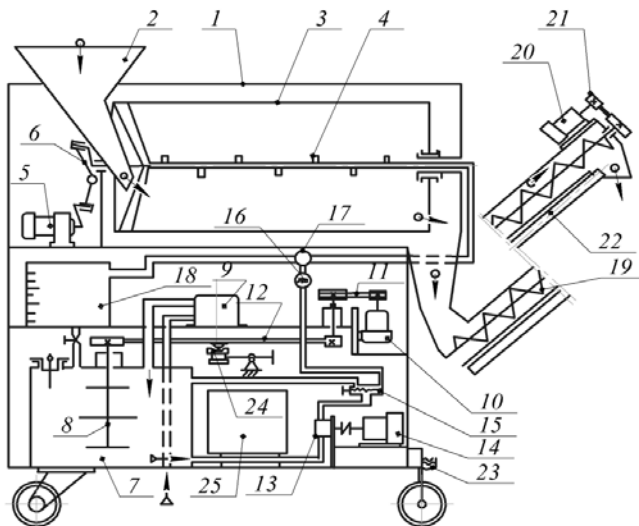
Схема дражиратора с горизонтальным барабаном: 1 – рама; 2 – загрузочный бункер; 3 – камера смешивания; 4 – штанги с форсунками; 5 – привод барабана; 6 – рычажная передача; 7 – бак рабочей жидкости; 8 – мешалка; 9 – насос; 10 – электродвигатель; 11, 12 – ременные передачи; 13 – насос; 14 – электродвигатель; 15 – дозатор; 16 – манометр; 17 – кран; 18 – мерная емкость; 19 – транспортер; 20 – электродвигатель; 21 – ременная передача; 22 – канал отсоса воздуха; 23 – механизм наклона барабана; 24 – муфта; 25 – пульт управления
